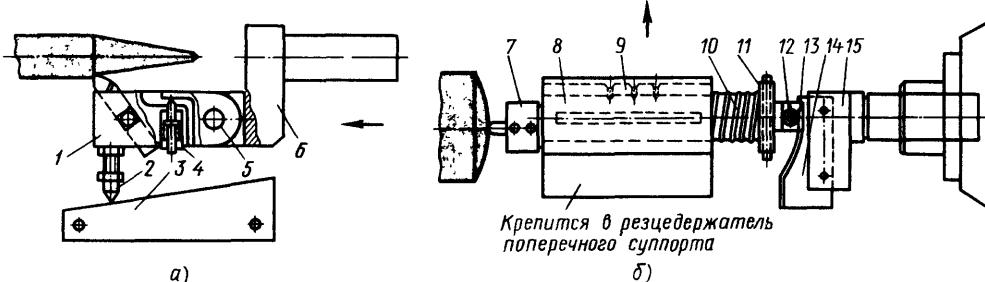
Приспособления для обработки фасонных поверхностей по копиру на токарно-револьверном станке:
